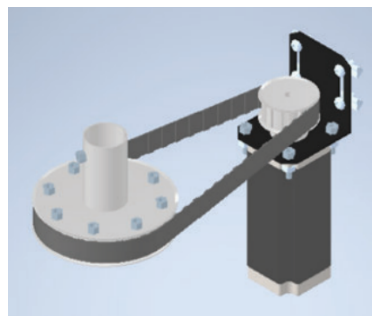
Representação do motor e mecanismo de transmissão de movimento relativo ao eixo A
